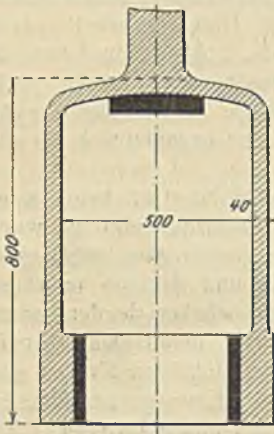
Zylinder zu einer hydraulischen Weinpresse.
